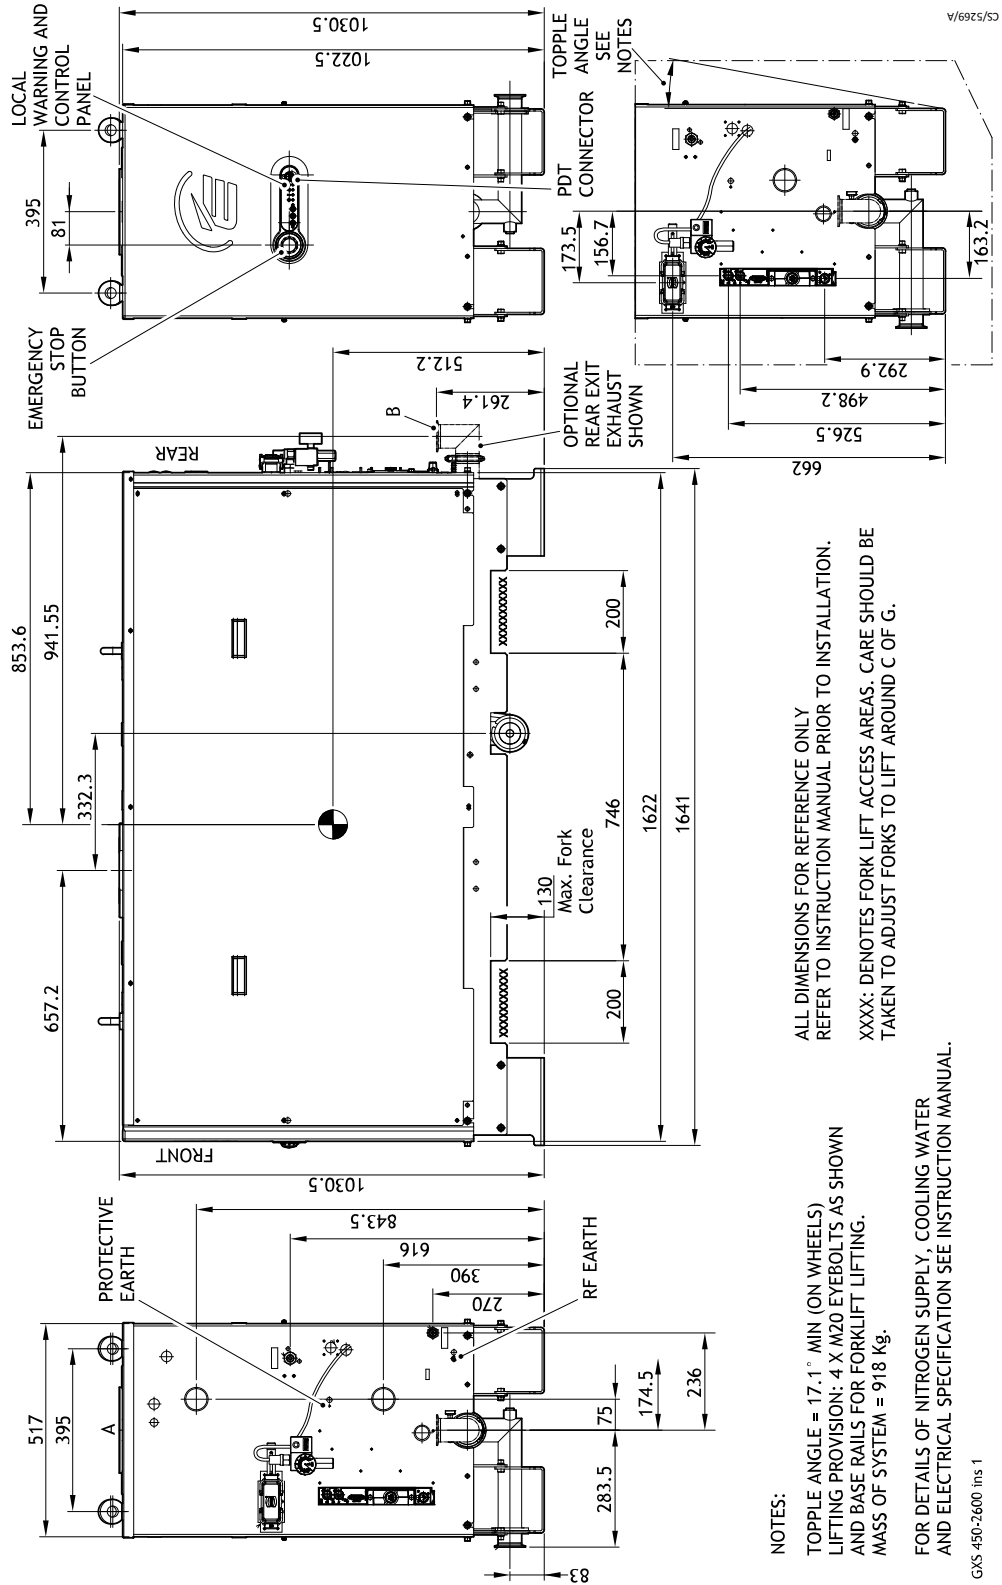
GXS750/2600 Installationszeichnung (Blatt 2)
